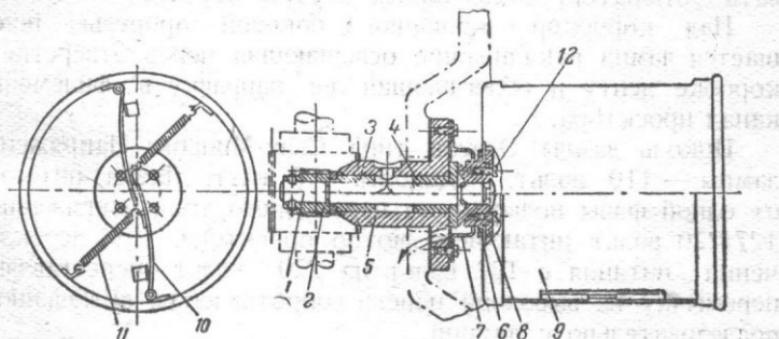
Обтюраторный механизм в разрезе: 1—вал; 2—малая шестерня; 3, 4—втулки; 5—подшипник; 6—фланец; 7—колпачок; 8—шайба; 9—обтюратор; 10—заслонка; 11—пружины; 12—винты
